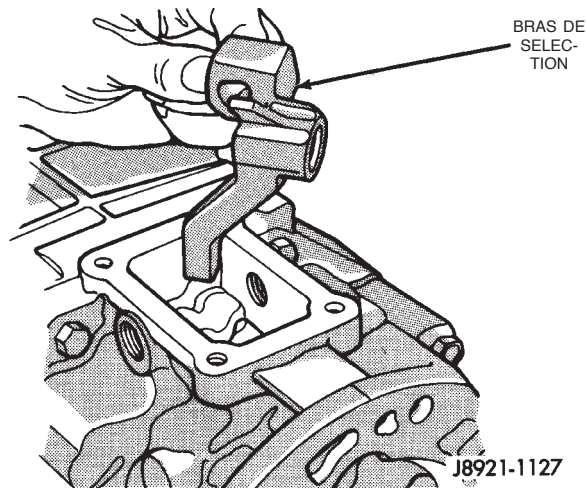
Pose de logement d'adaptateur/carter arrière—vue type
